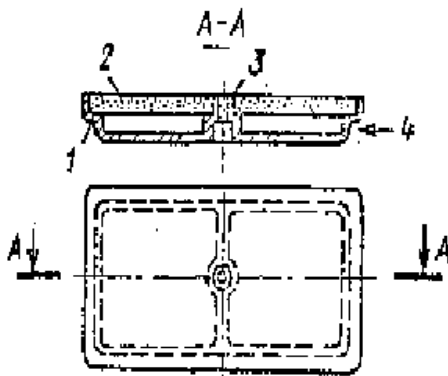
Коробка с пористой аэроплиткой: 1 – металлический корпус; 2 – аэроплитка; 3 – крепление плитки к корпусу; 4 – подача воздуха под плитку
